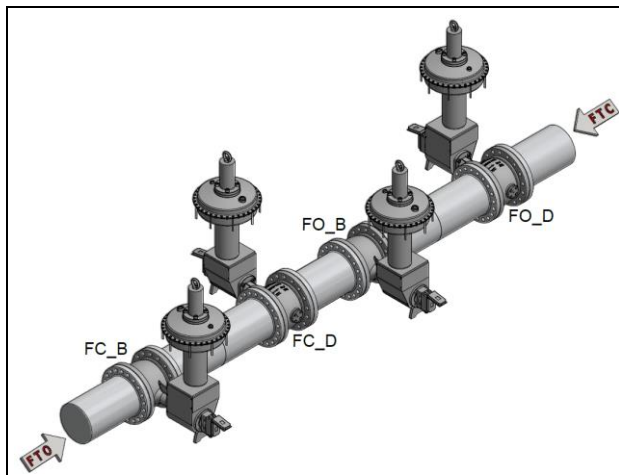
Standard-Einbaulagen - horizontale Rohrleitung
